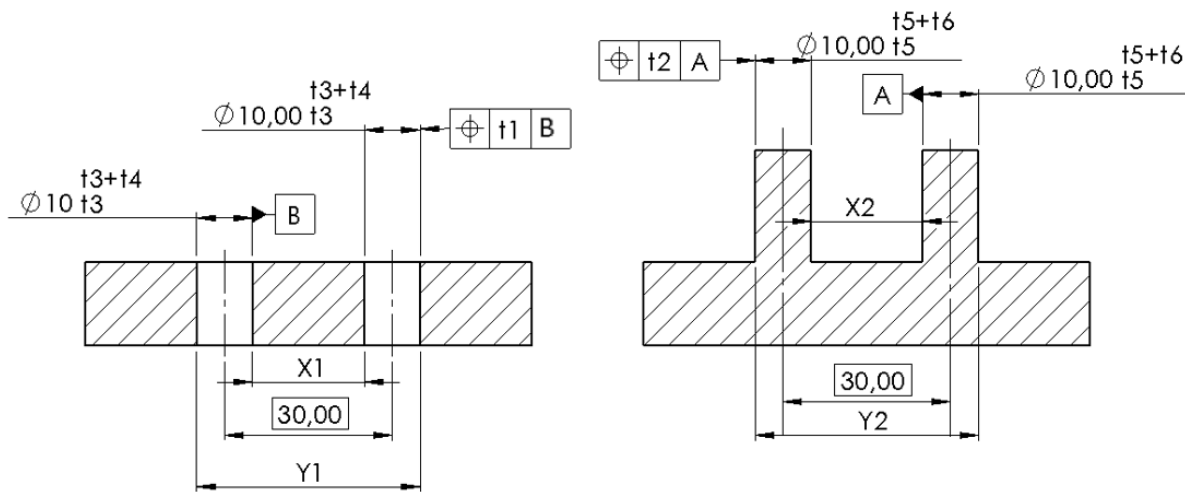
Plan simplifié des deux pièces à assembler
